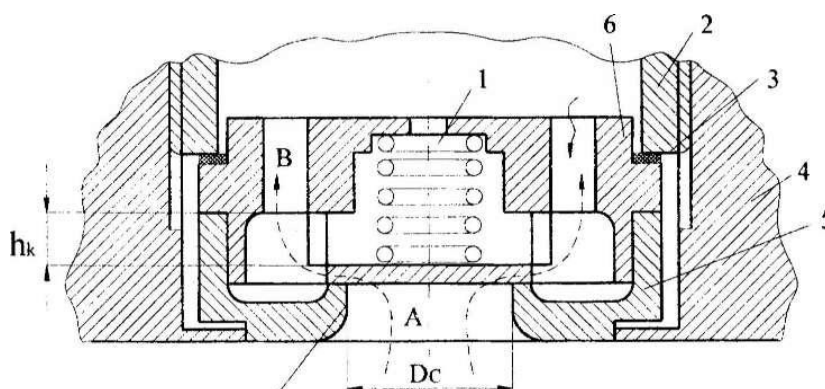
Самодействующий клапан с плоской тарелочкой: 1 - пружина; 2 - втулка; 3 - уплотнение (прокладка); 4 - крышка цилиндра; 5 - седло; 6 - ограничитель; 7 - тарелка; А, В – отверстия
